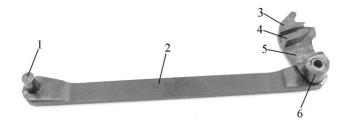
Спусковая тяга с рычагом взвода: 1 — цапфа; 2 — спусковая тяга; 3 — разобщающий выступ; 4 — выступ самовзвода; 5 — рычаг взвода; 6 — пяточка рычага взвода
